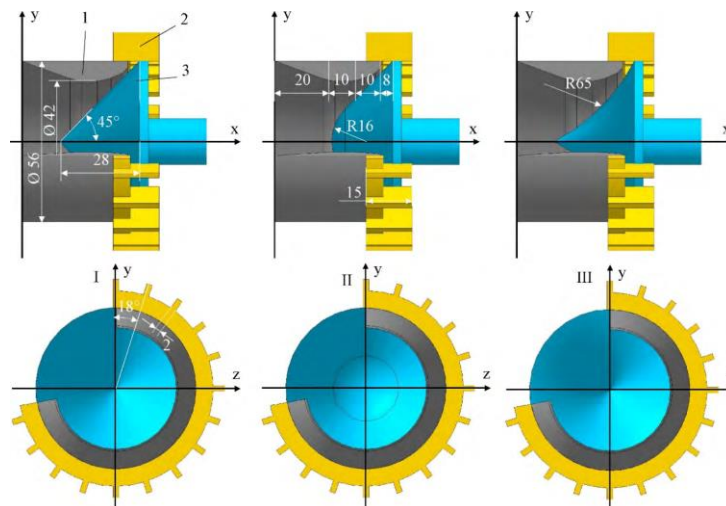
Конструктивні варіанти формувальної насадки експандера кормів: 1 – циліндрична частина; 2 – корончата гайка; 3 – конус; I – конус традиційної форми; II – конус із заокругленою поверхнею; III – увігнутий конус.
